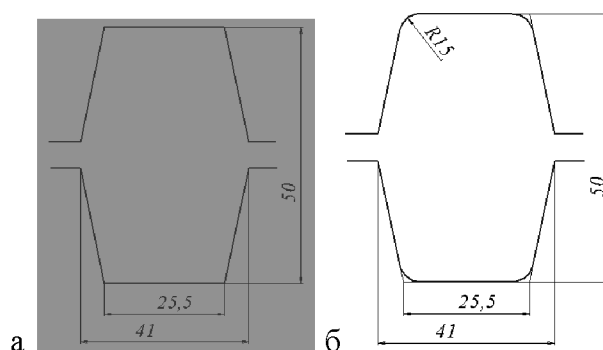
Ребровой калибр I-й клетки чистовой линии стана 325:
